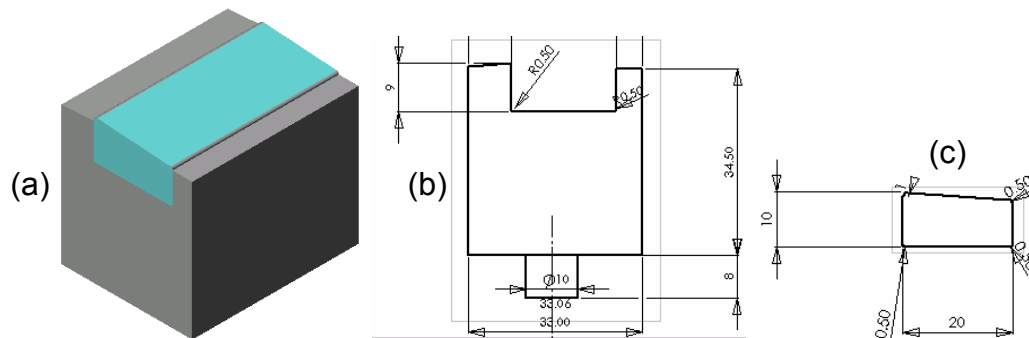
Moldes especiais com inserts: (a) perspectiva do molde com o inserto; (b) vista da base do molde; (c) vista do inserto.
